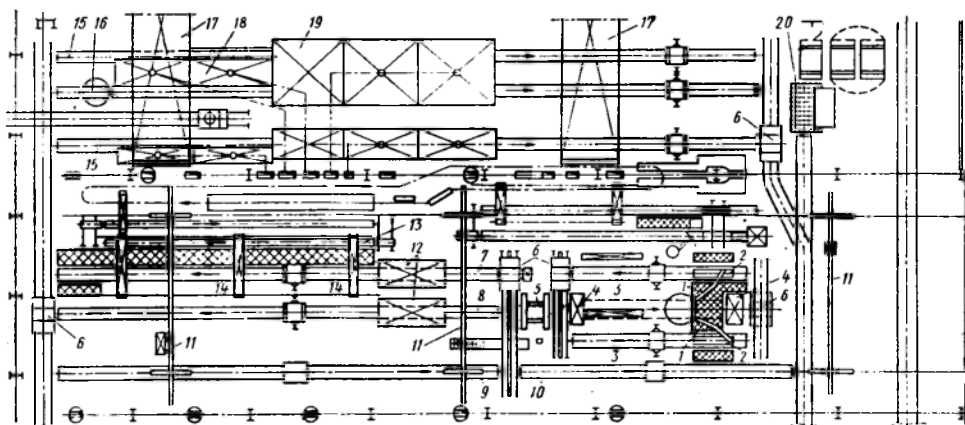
Комплексно-механизированная линия изготовления отливок в формах из ХТС:
